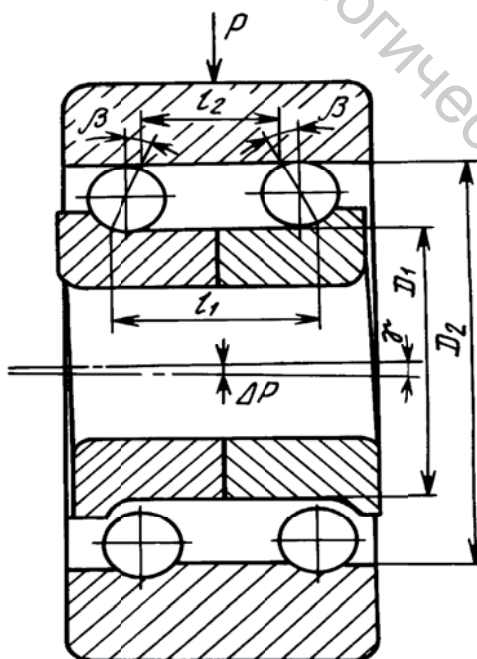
Двухрядный шариковый радиально-упорный подшипник
